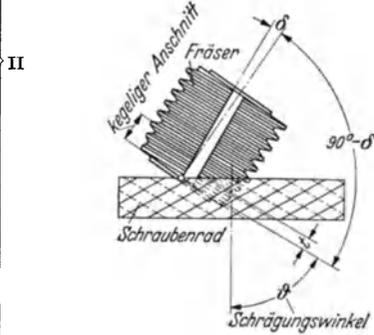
FräserEinstellung beim Wälzfräsen von Schraubenrädern.
